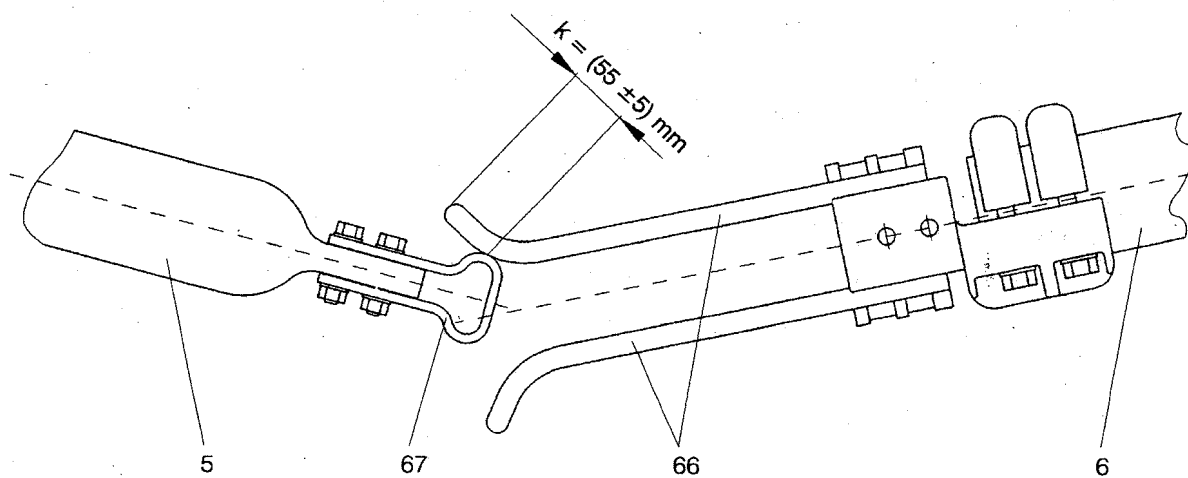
Установка тяг разъединителя: главные контакты разъединителя, зацепление
